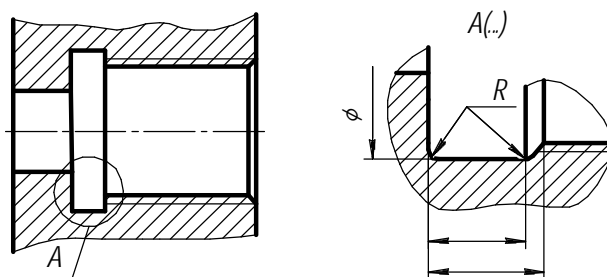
Проточки для выхода резьбонарезающего инструмента в отверстиях
